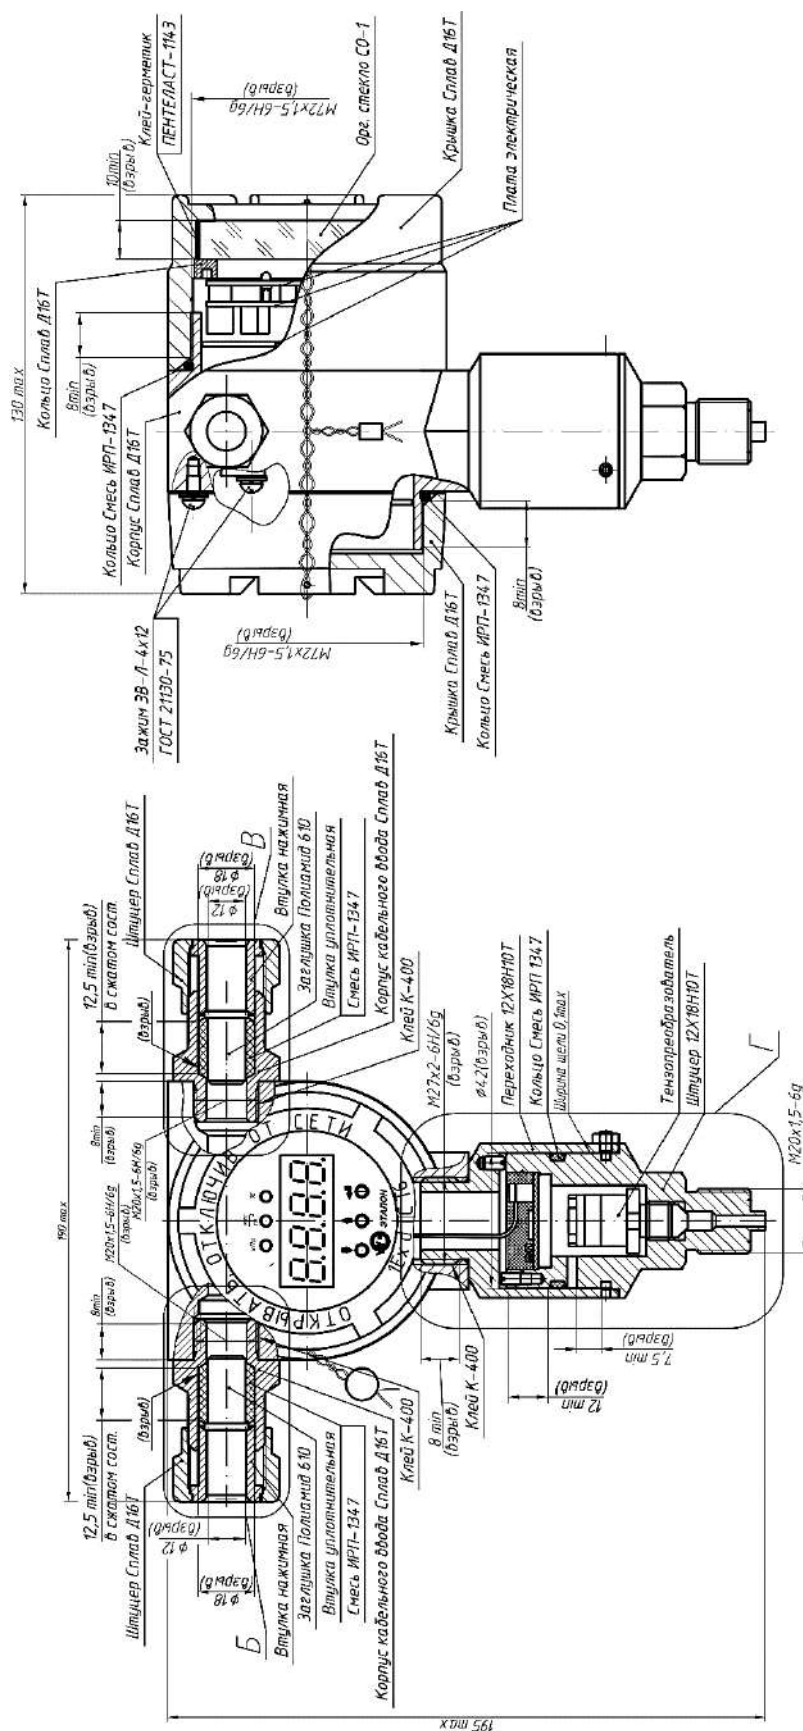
Чертеж взрывозащиты датчиков в корпусе из алюминиевого сплава
